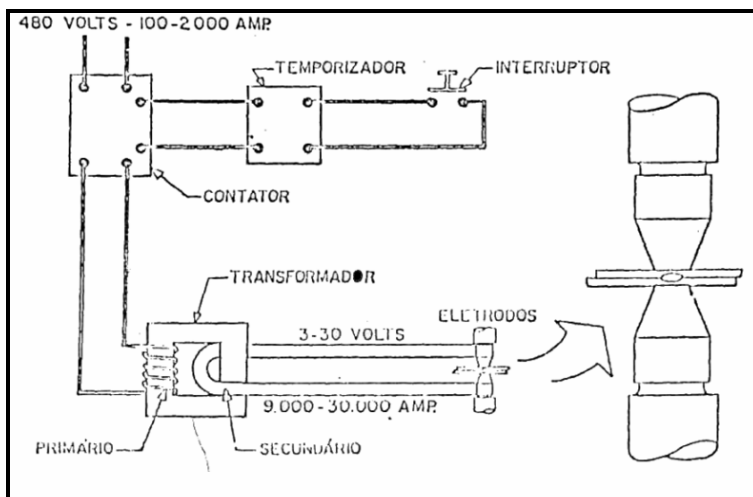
ESQUEMA ELÉTRICO PINÇA DE SOLDA PONTO
